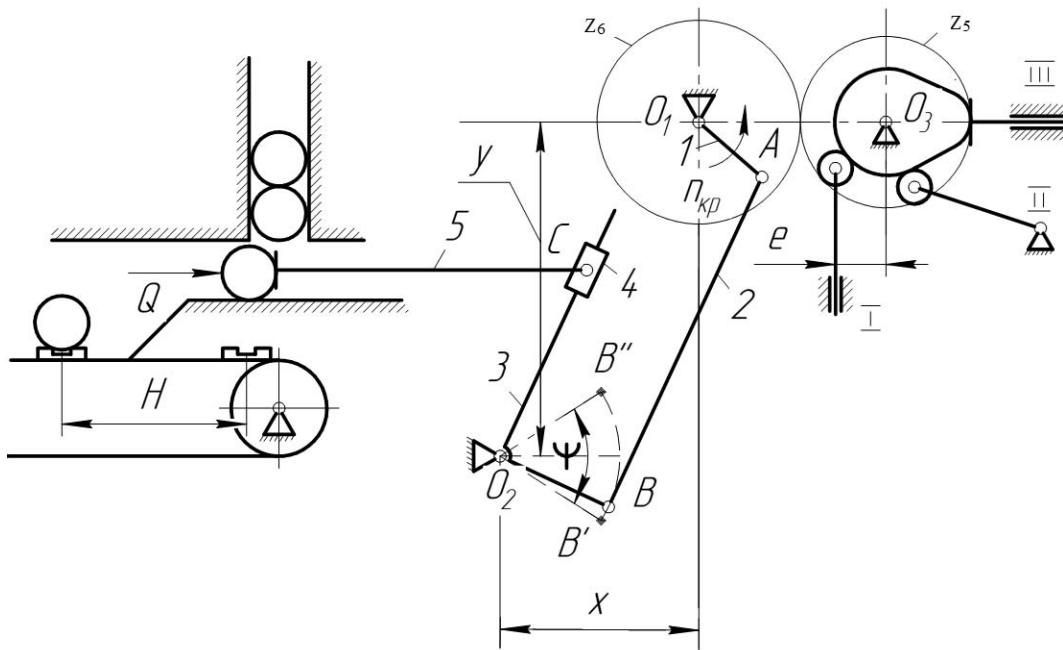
Механизм устройства подачи деталей из накопителя
